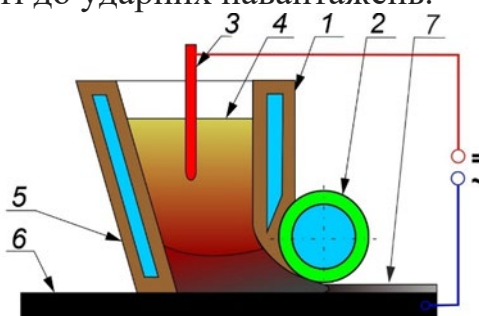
Схема здійснення процесу горизонтальної електрошлакового наплавлення плоскої поверхні [2]: 1 – кокіль-кристалізатор; 2 – валок-кристалізатор; 3 – наплавочний дріт; 4 – шлакова ванна; 5 – металева ванна; 6 – наплавлений метал
